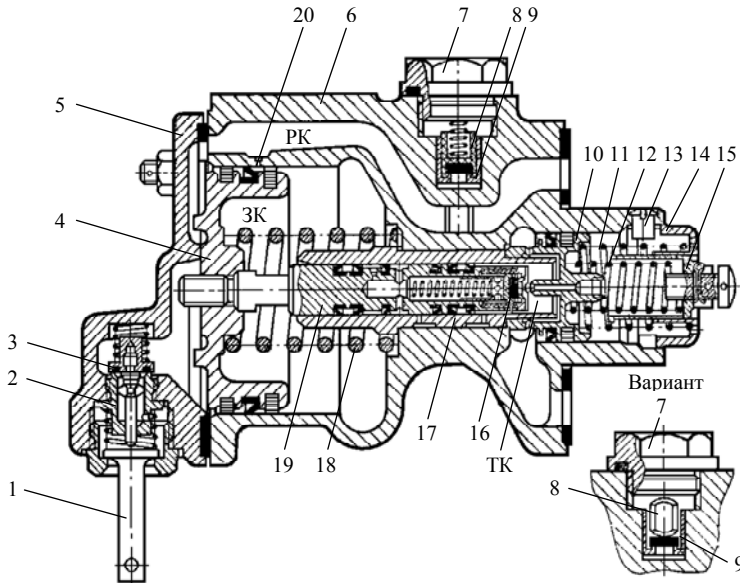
Главная часть № 270-023 воздухораспределителей № 270-002, 270-005 и 483
